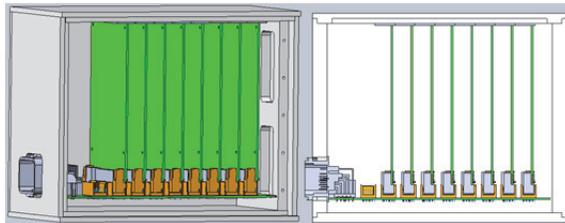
Внешний вид центрального блока управления в стандартном корпусе
